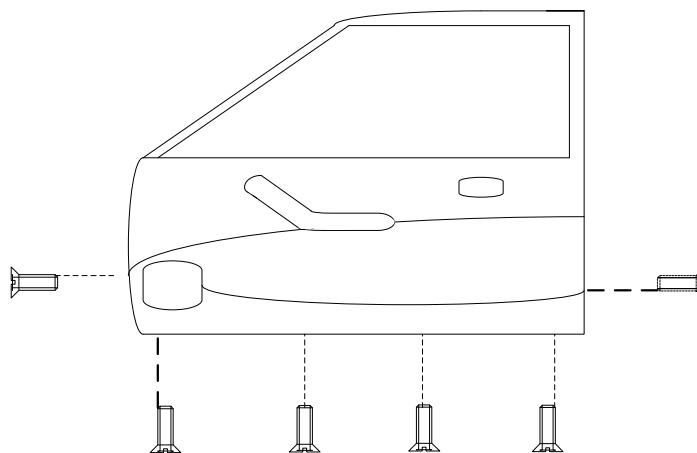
Desmontaje de la Tapicería de las Puertas
